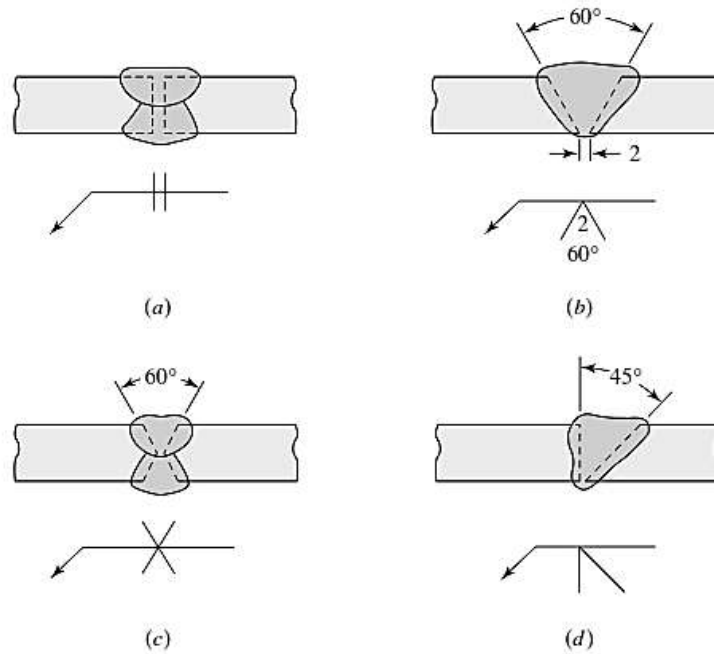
Soldaduras a Tope, sometidas a tracción o compresión: (a) tope con extremos rectos; (b) bisel a 60°; (c) doble bisel a 60°; (d) bisel simple a 45°.
